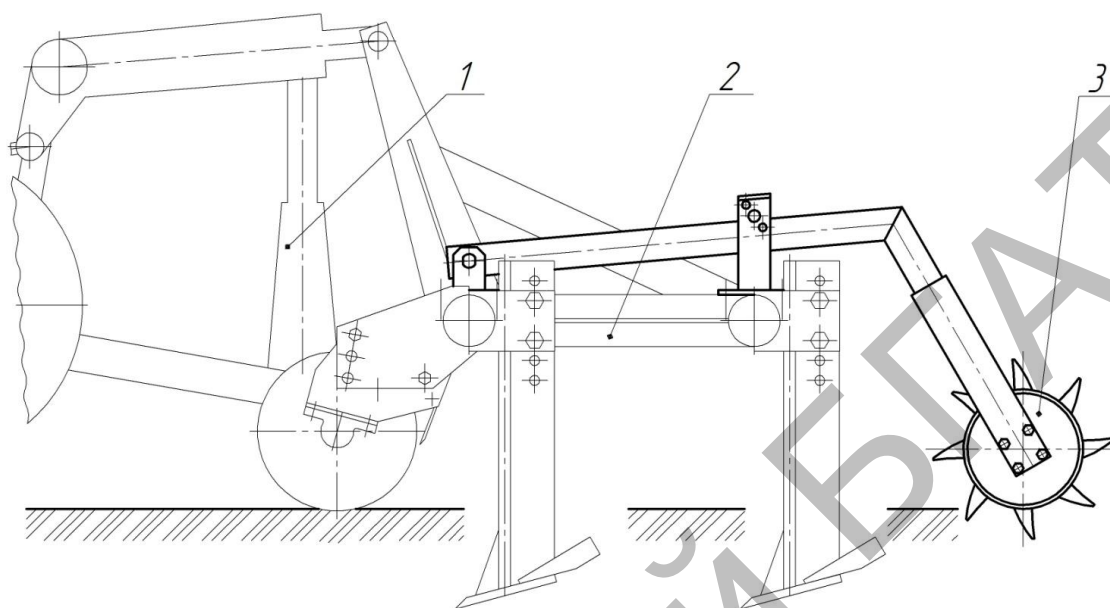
Схема агрегата: 1- трактор; 2 - плуг ПЧН-3,2; 3 – вибрационный каток
